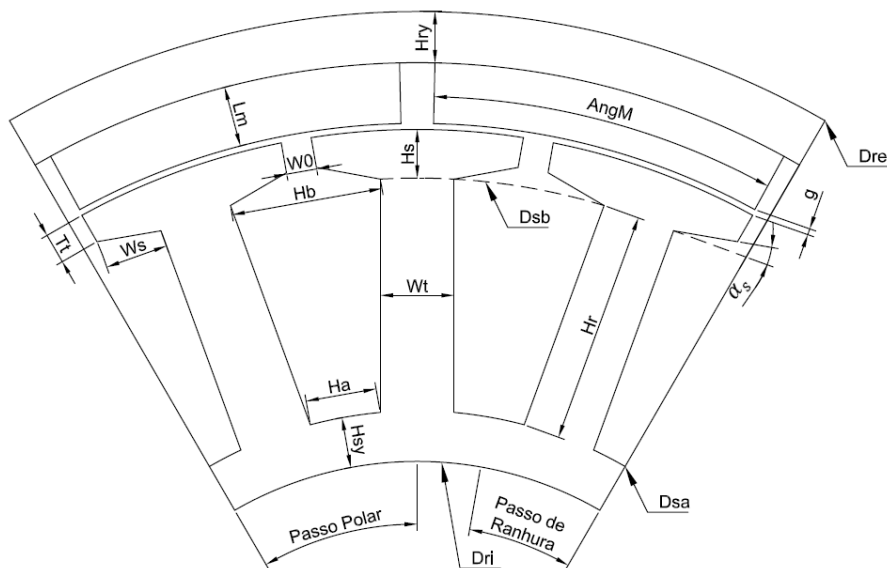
Nomenclatura para o dimensionamento do material ferromagnético do motor com o rotor externo [Autor].
